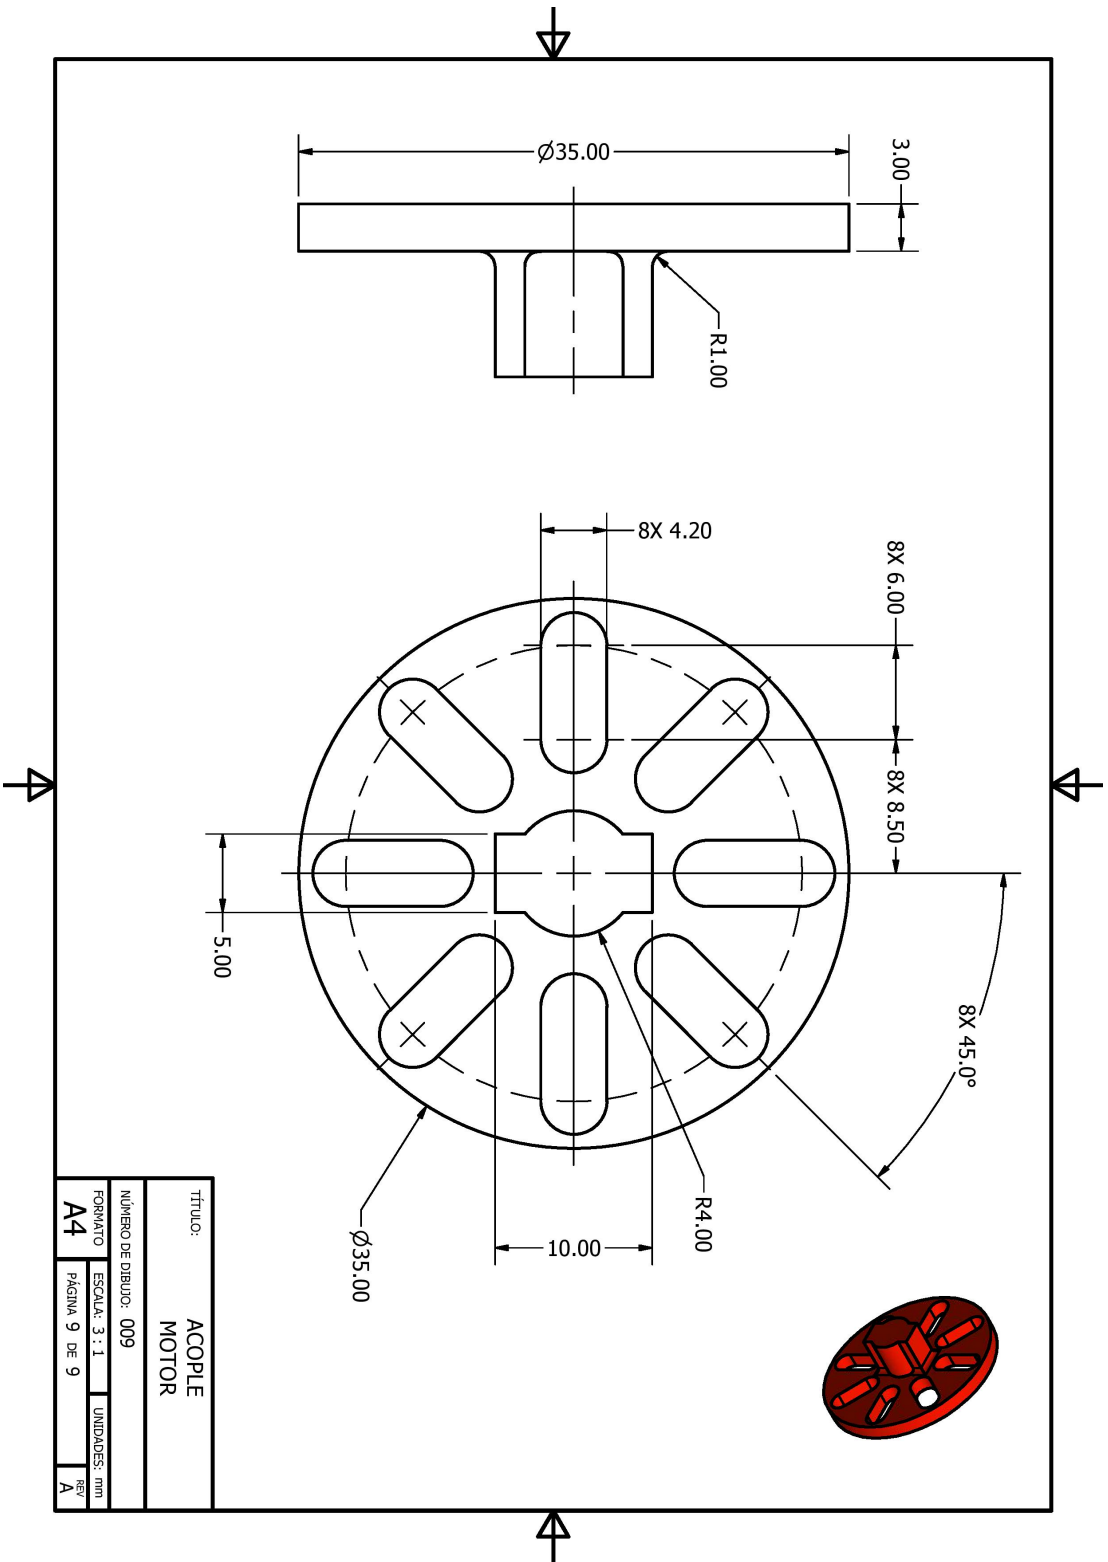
Plano de acople de motor del engrane recto para mecanismo híbrido
